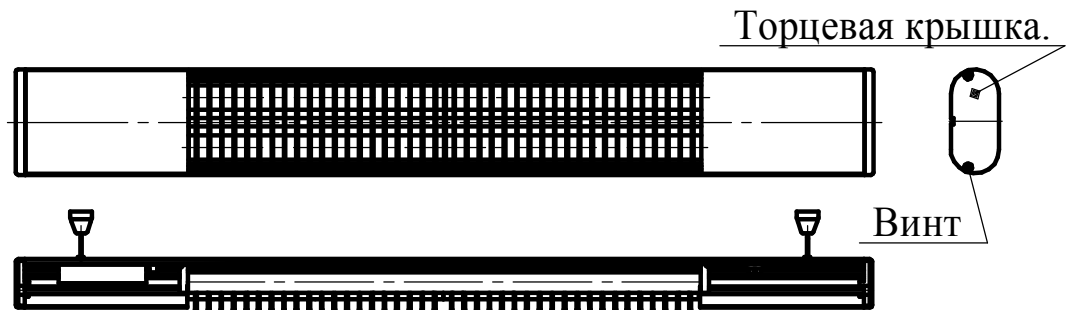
1. Узел подвеса, 2. Корпус в сборе, 3. Крышка, 4. Решётка или рассеиватель.
